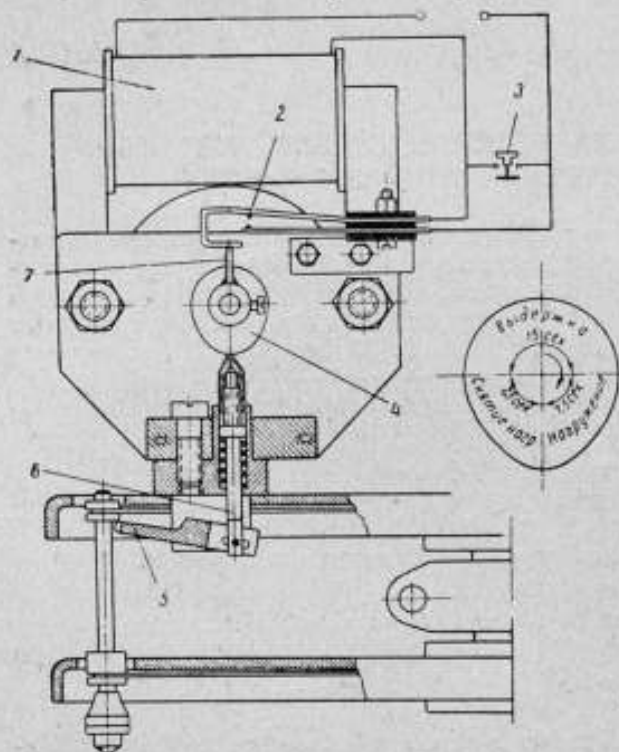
Схема приспособления для автоматического нагружения ПМТ-3.
